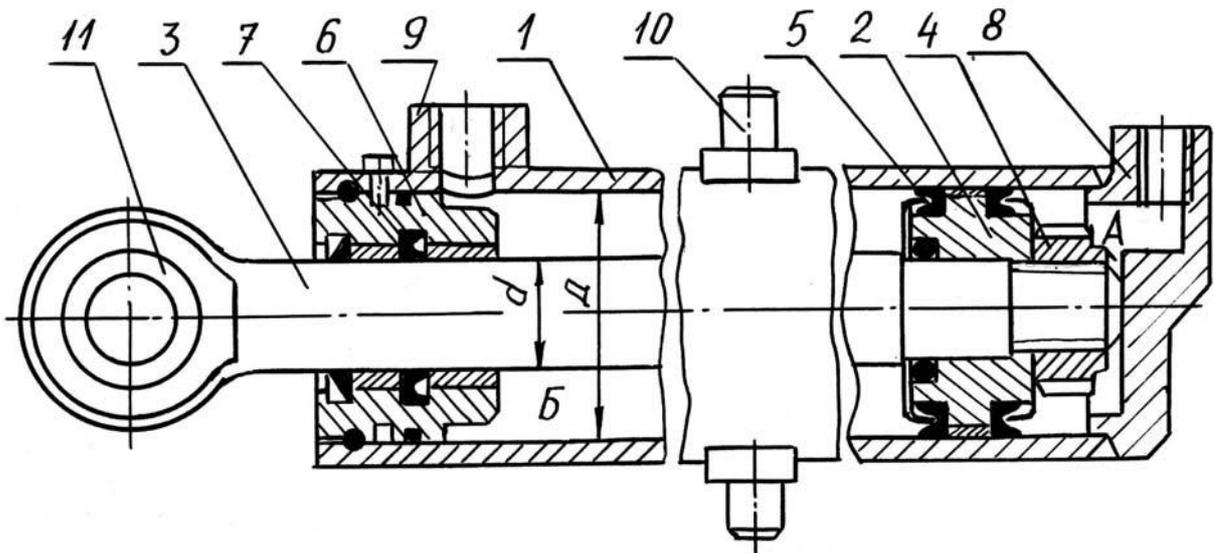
Гидроцилиндр бульдозера ДЗ-42
